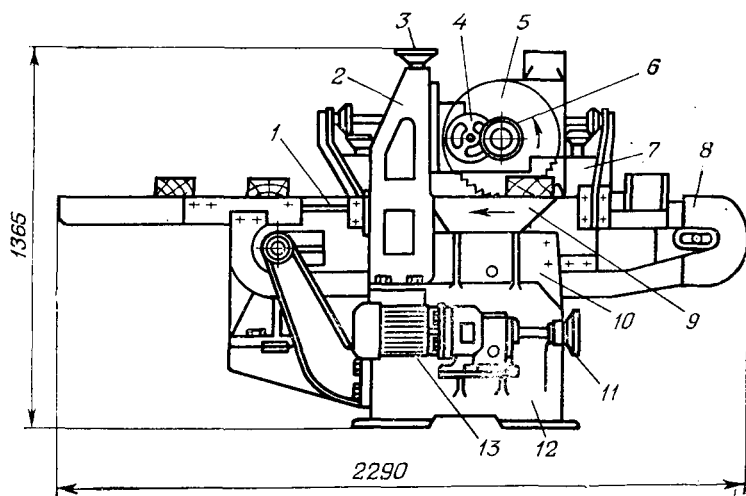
Концервнительный двухпильный станок с конвейерной подачей
